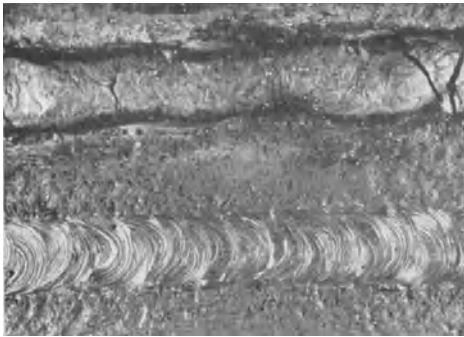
Aussehen von Schweißraupen mit und ohne Schlacke.
